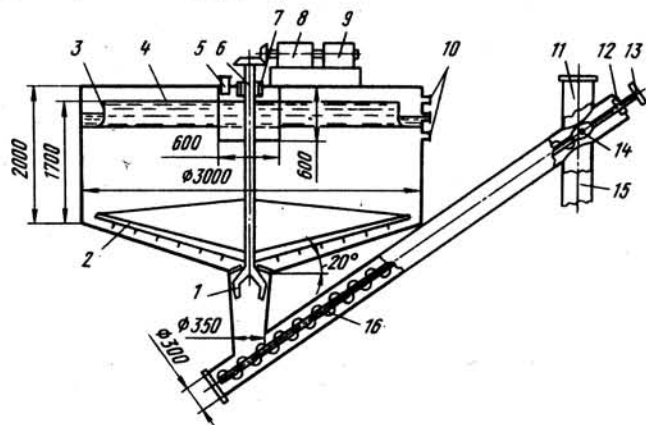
Схема сгустителя Дорра: 1 — очистительные щетки; 2 — скребковый механизм; 3 — сливной карман; 4 — успокоительная корзина; 5 — штуцер для пульпы; 6 — вал; 7 — сальниковое уплотнение; 8 — редуктор; 9 — электродвигатель; 10 — сливные штуцера; 11 — очистной люк; 12 — сальник; 13 — приводная шестерня; 14 — шарнир Гукса; 15 — разгрузочный патрубок; 16 — наклонный шнек
